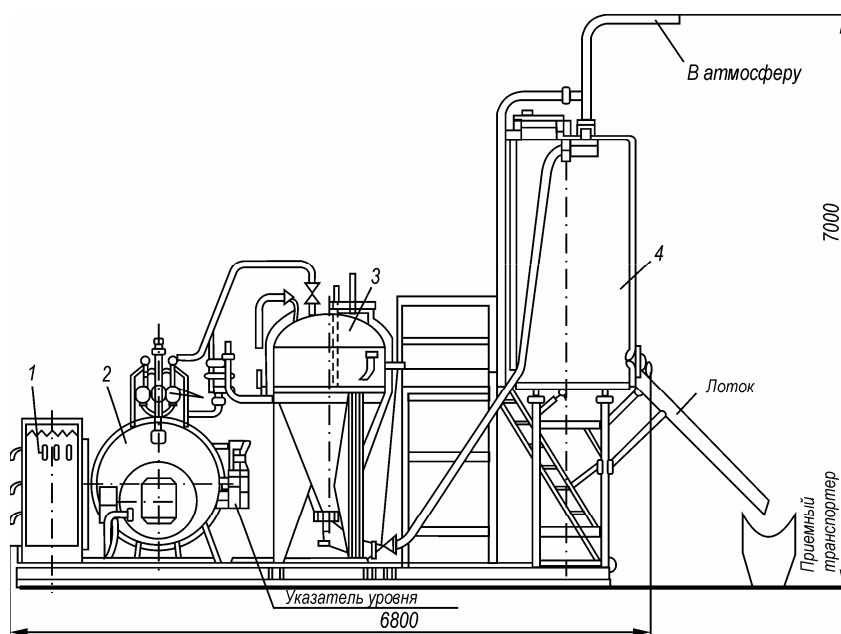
Схема установки «Лескорм-1» для гидробаротермической обработки сырья:
